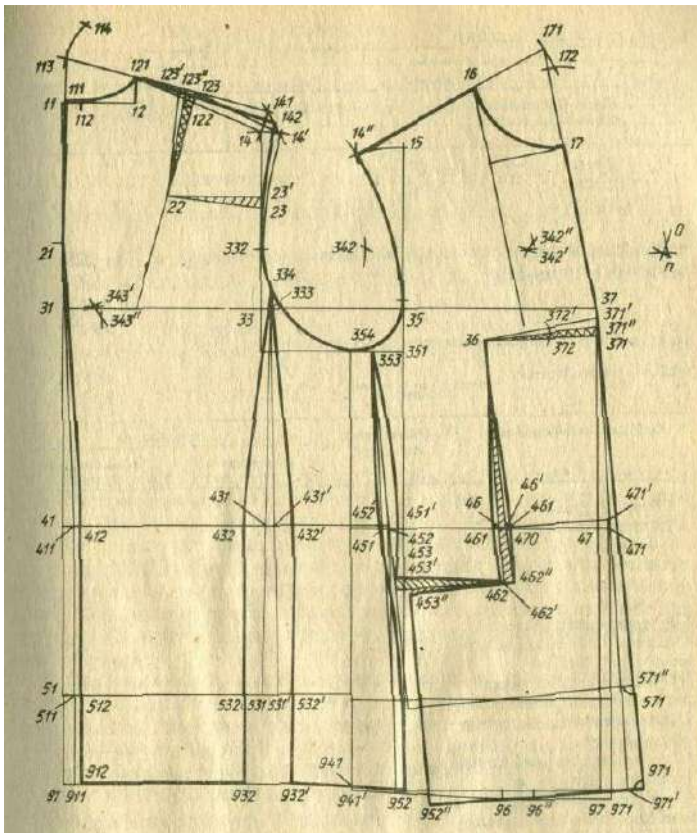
Чертеж базовой конструкции мужского пиджака размера 176-100-88
